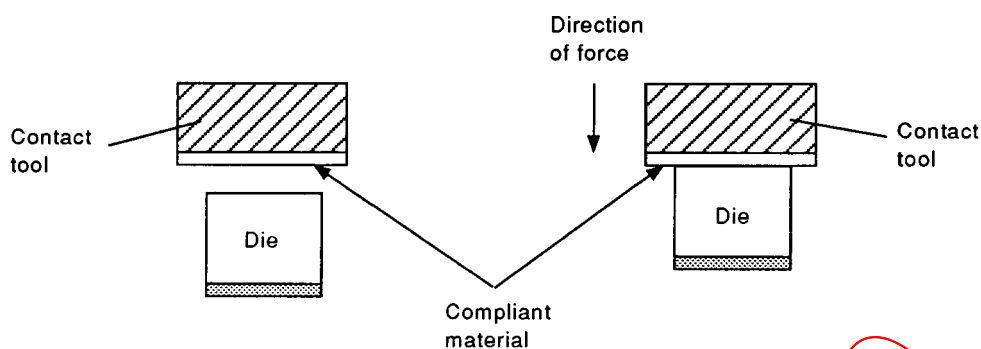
Alignement de l'outil avec la pastille (vue de dessous)
